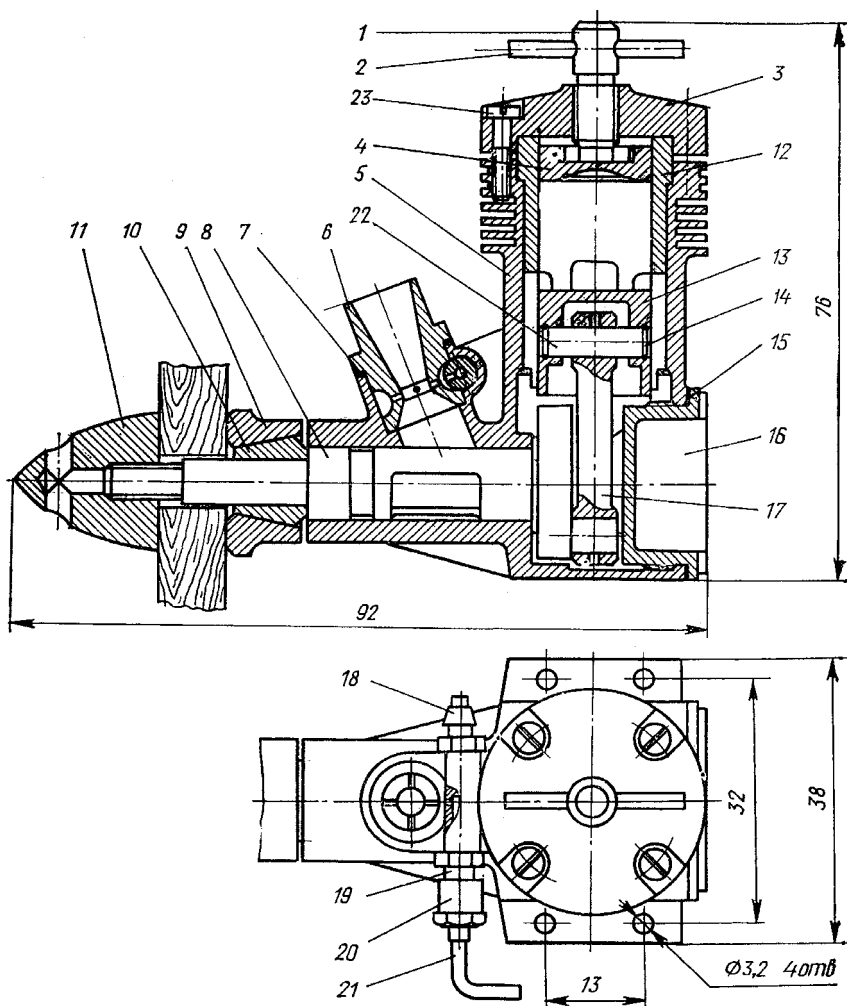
Детали микродвигателя ЦСТКАМ-2,5 Д:
